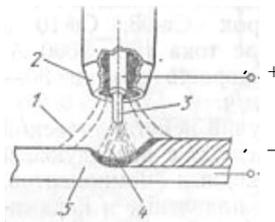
Схема дуговой сварки в среде защитного газа
